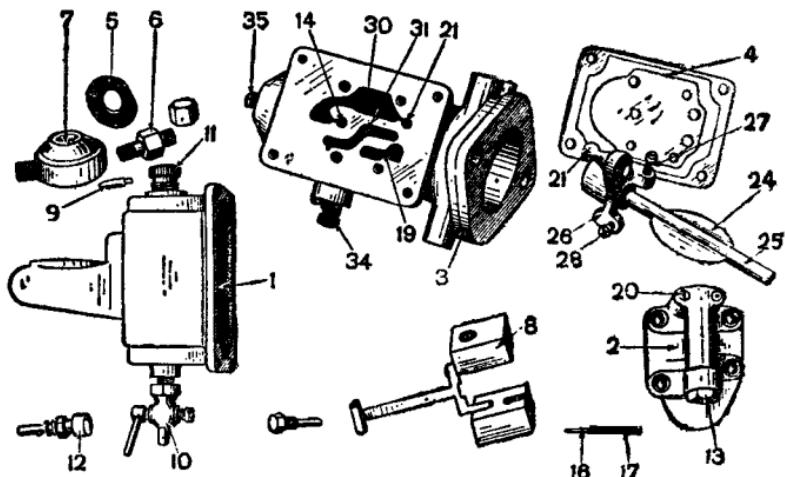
Детали карбюратора двигателя ЧТЗ.
